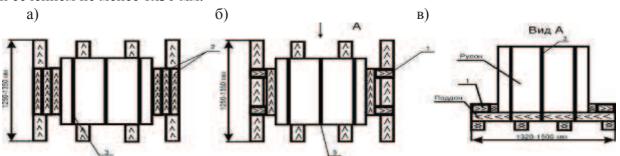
Крепление рулона на поддоне 1 — продольный брусок сечением 100х100 мм; 2 — набор поперечных брусков сечением 100х100 мм; 3 — металлическая лента
